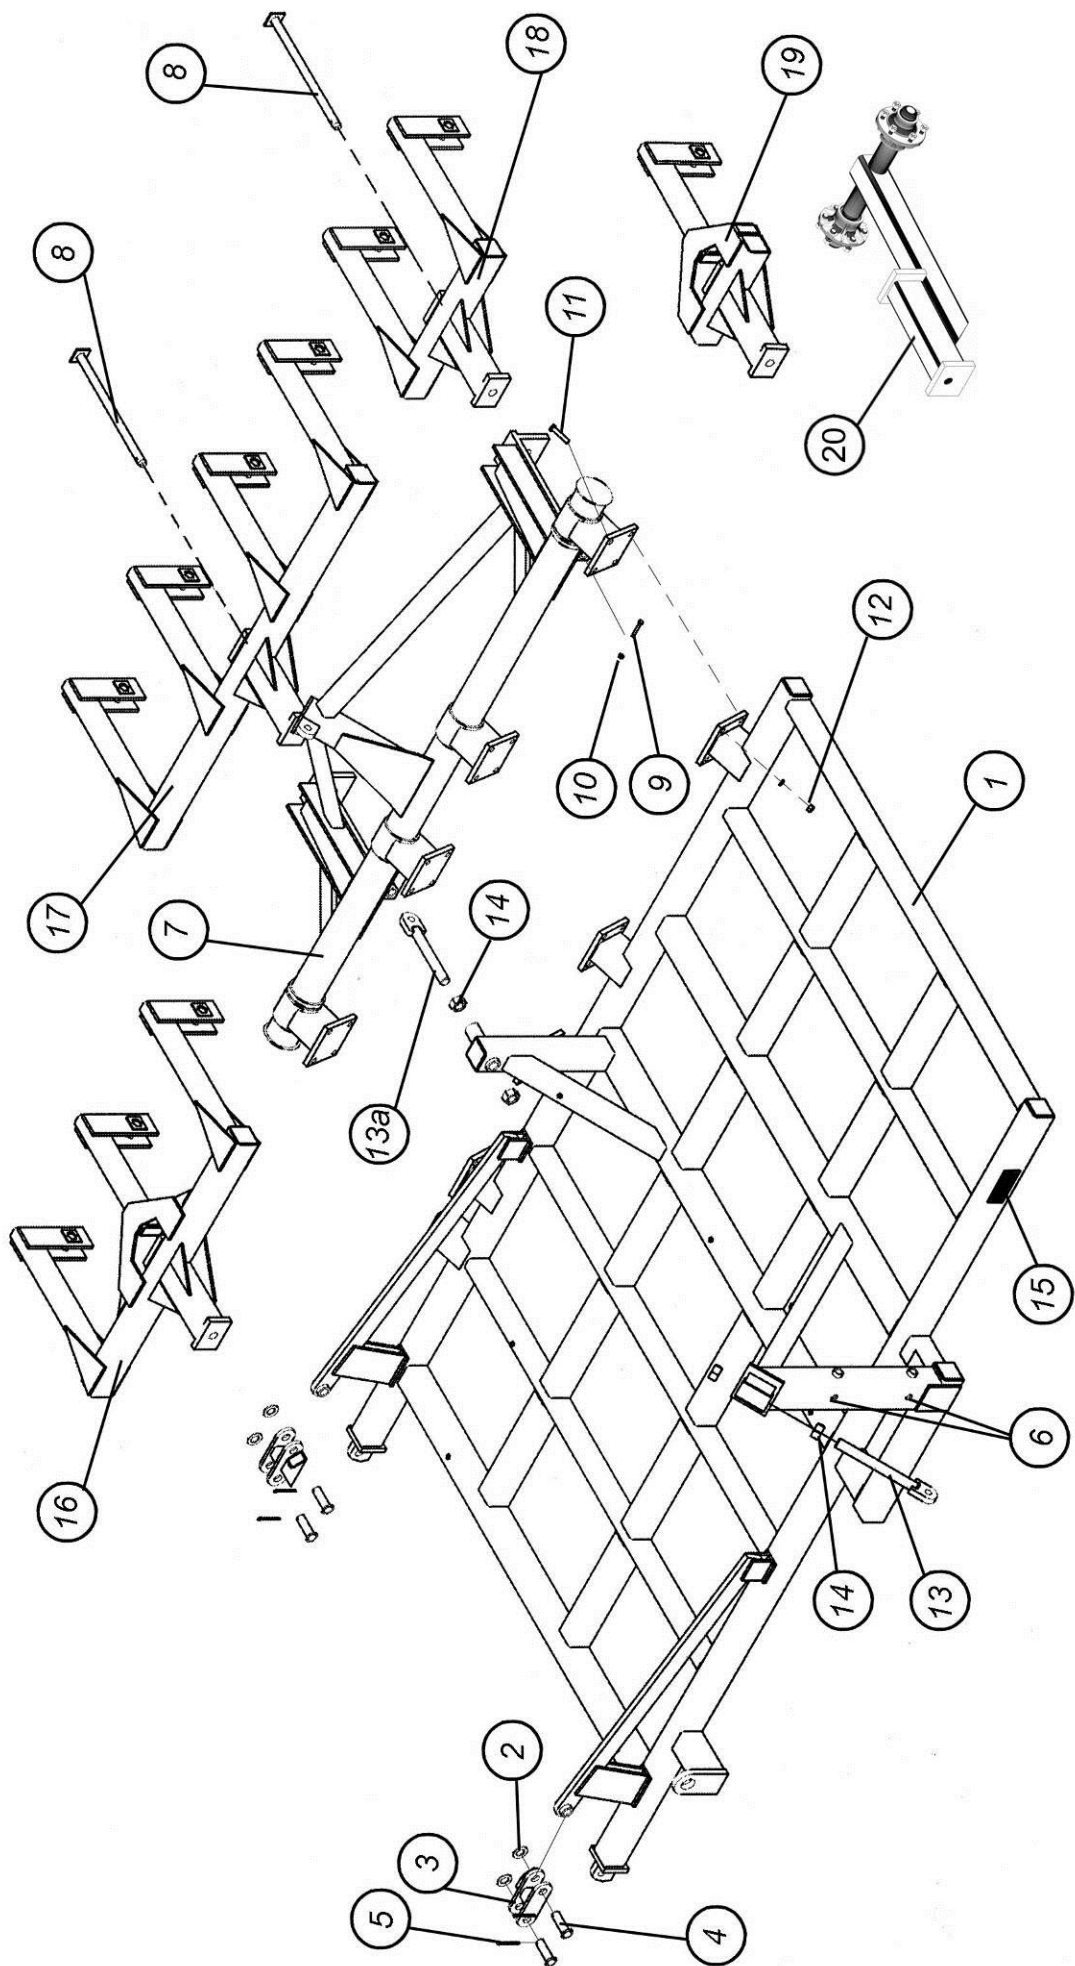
Боковая рама с узлом качающегося вала и подвеской прикатывающих колес
